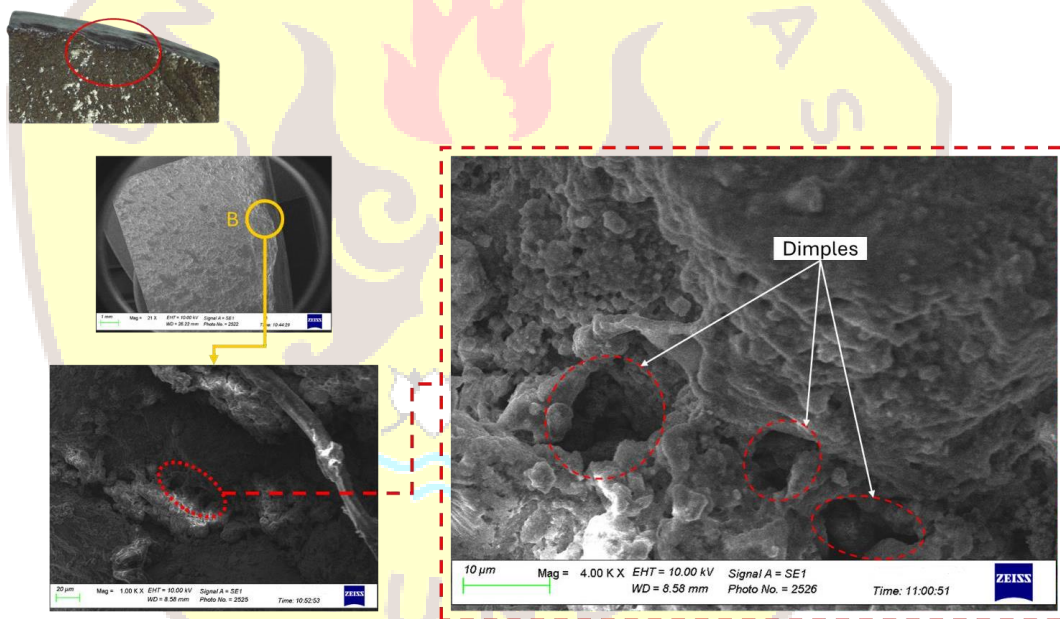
SEM Bagian Initial Crack terdapat Crack dan Micro Crack
